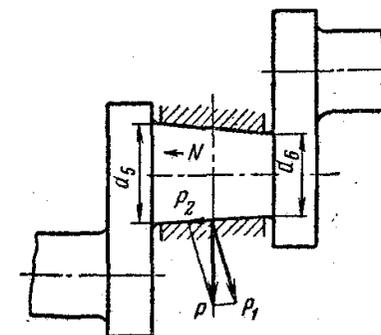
Расположение конусных шеек вала коренной шейки
